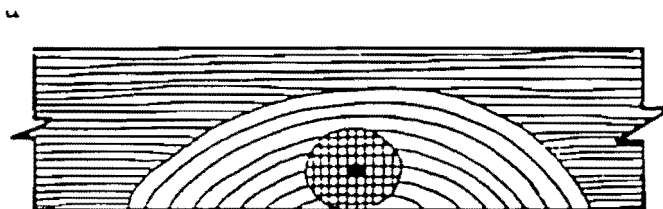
Zona de fractura frágil (sombra blanca) alrededor de un defecto, que sirve como iniciador de una fractura progresiva por fatiga (marcas de playa).
